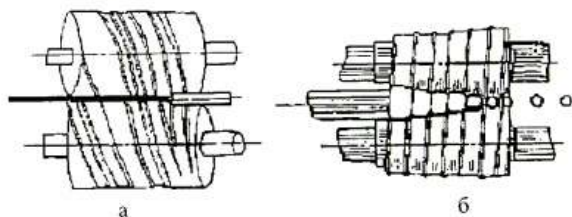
Схеми періодичної прокатки заготовок:
